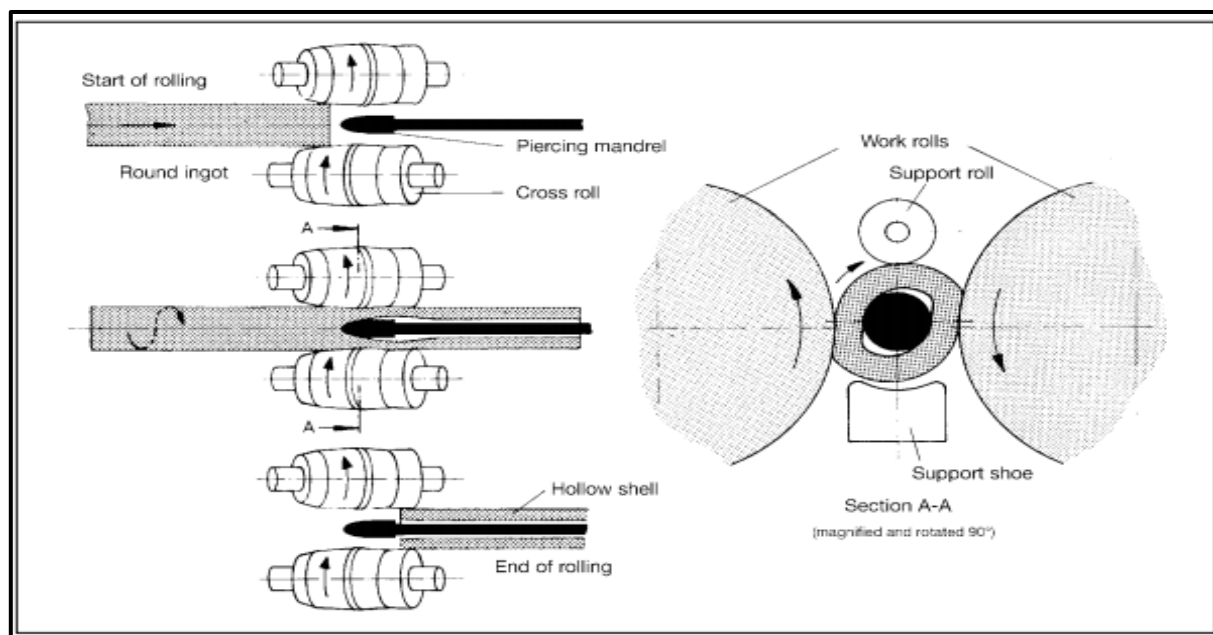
Fabrication des tubes sans soudures [12].
